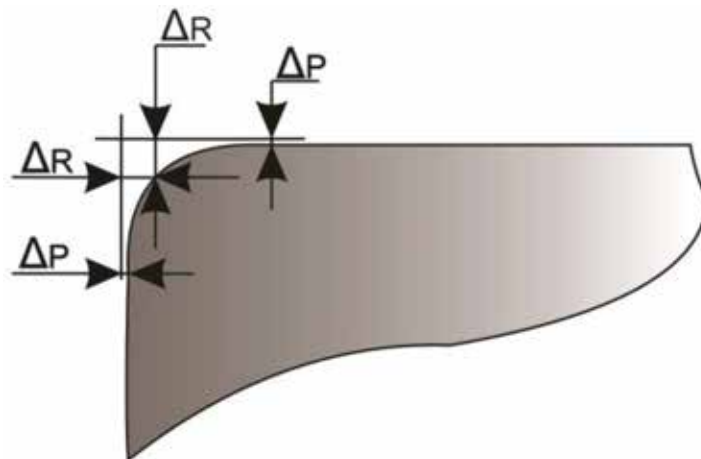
Схема заокруглення кромки під час віброполірувальної обробки [12]
